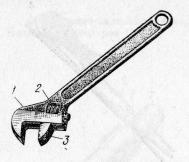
1 — корпус; 2 — червяк; 3 — губка подвижная с рейкой
